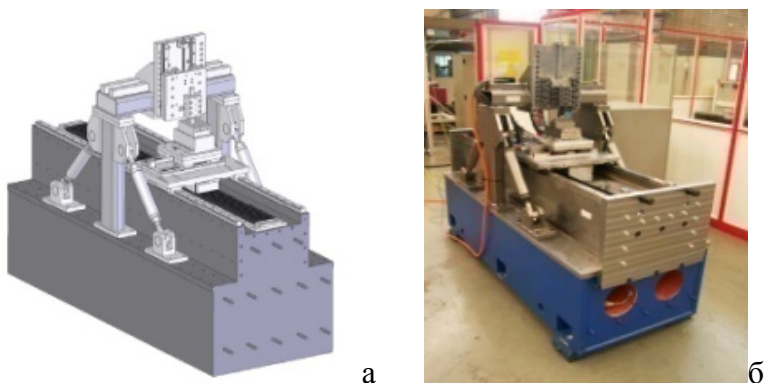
Схема станда (а) и его общий вид (б)
